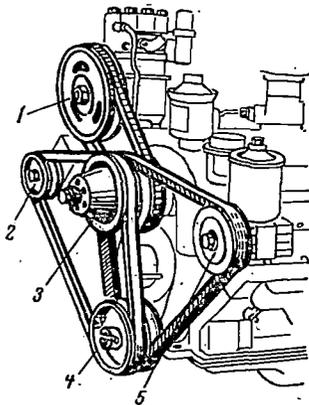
Приводные ремни и шкивы двигателя ЗИЛ-130:
